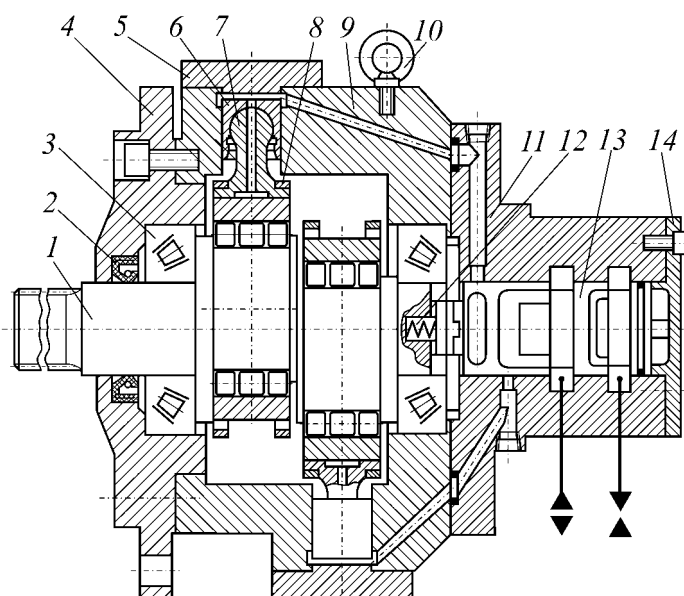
Радиально-поршневой гидромотор серии МРФ: 1 – коленчатый вал; 2 – уплотнительная манжета вала; 3 – специальные роликовые подшипники; 4, 5, 11, 14 – крышки; 6 – поршни; 7 – шатуны; 8 – фиксирующие кольца шатунов; 9 – корпус; 10 – рым; 12 – пружина; 13 – распределительный вращающийся золотник, соединенный с валом крестовой муфтой Ольдгейма
